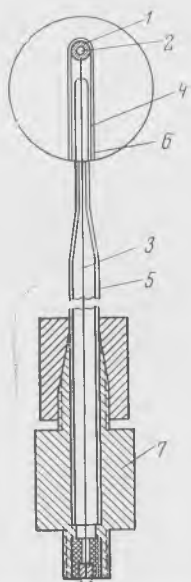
Конструкция сверхминиатюрного сферического гидрофона
